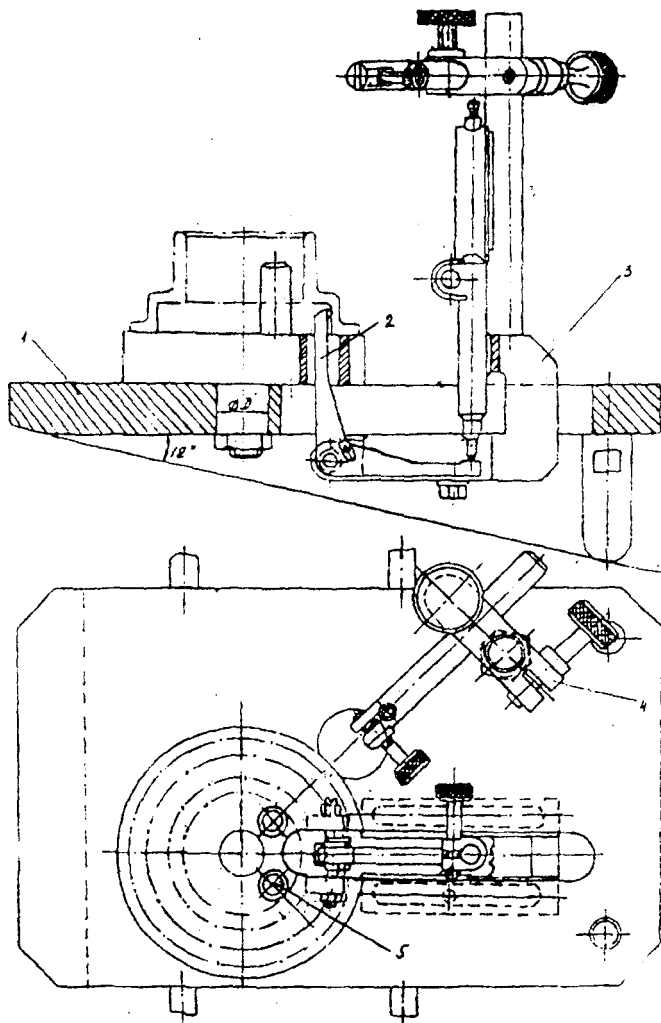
Приспособление для контроля биений диаметров деталей типа "втулка"
